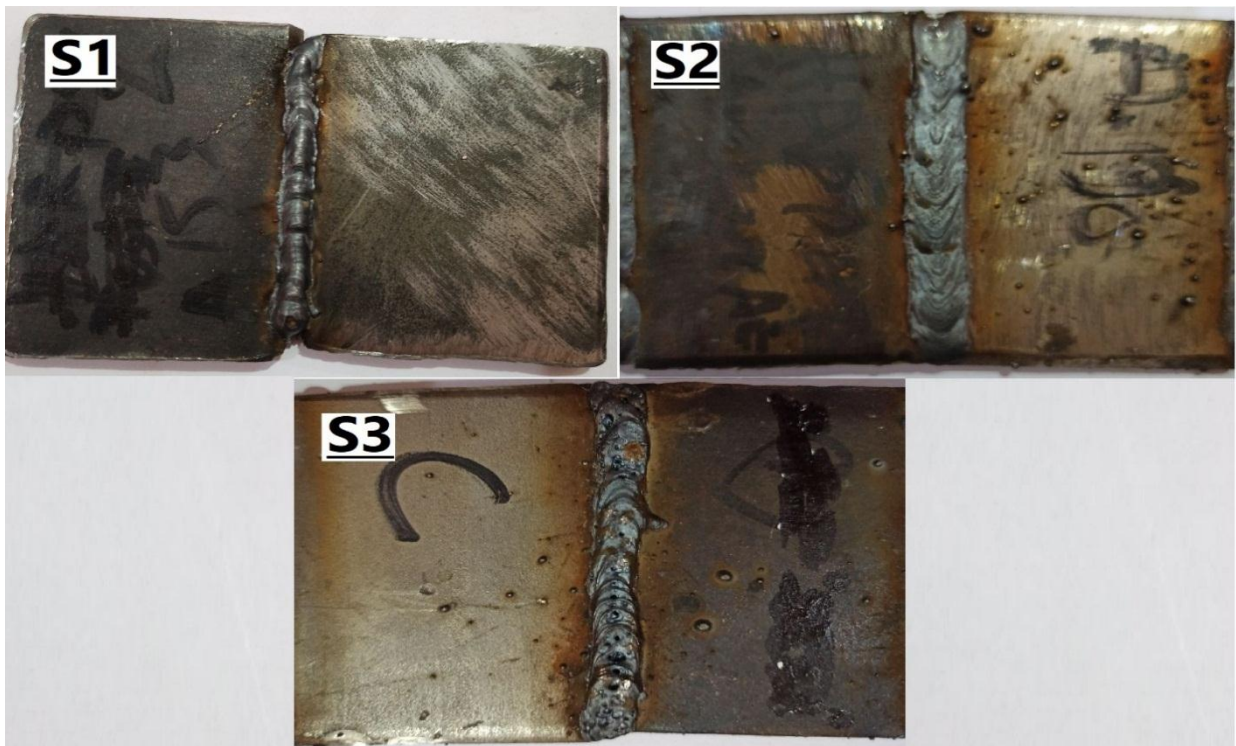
La forme de la plaquette soudage différent métallique (après soudage).
